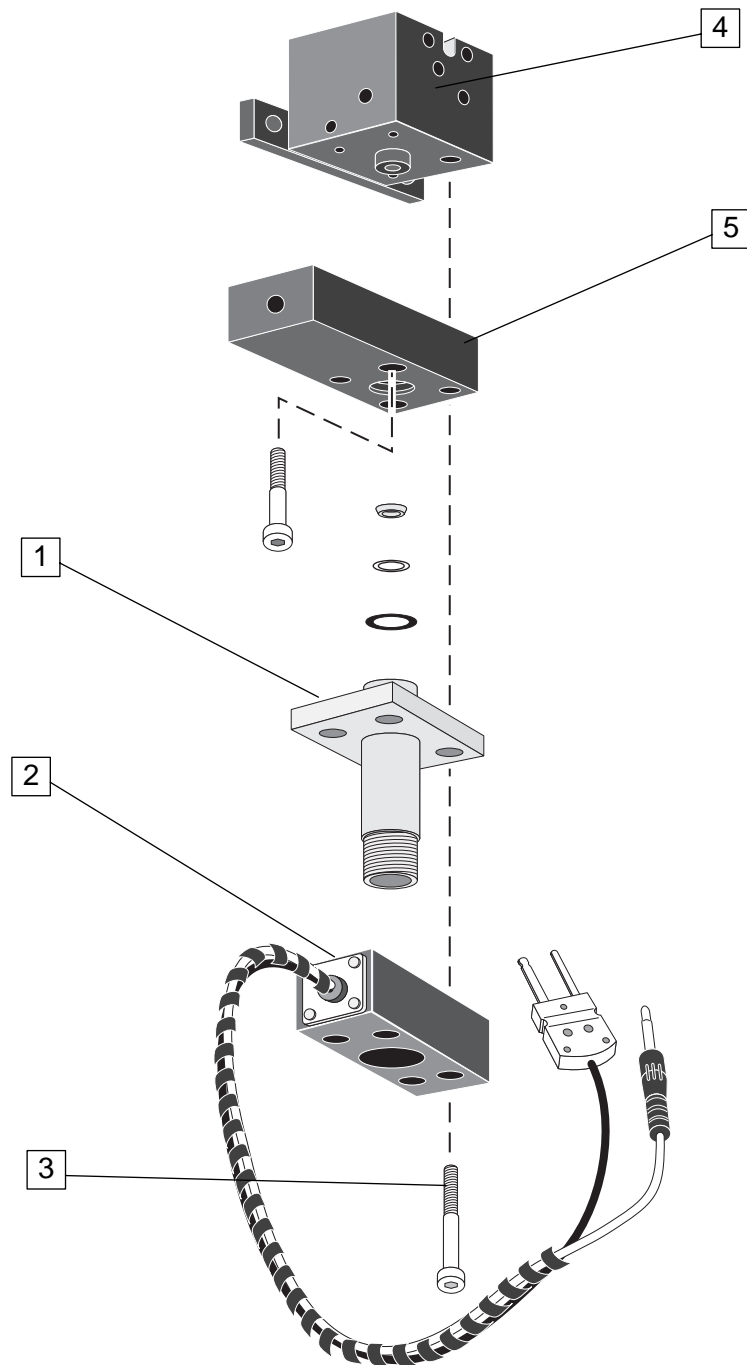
Zusammenbau von unterem und oberem Gehäuse sowie Magnetventil
